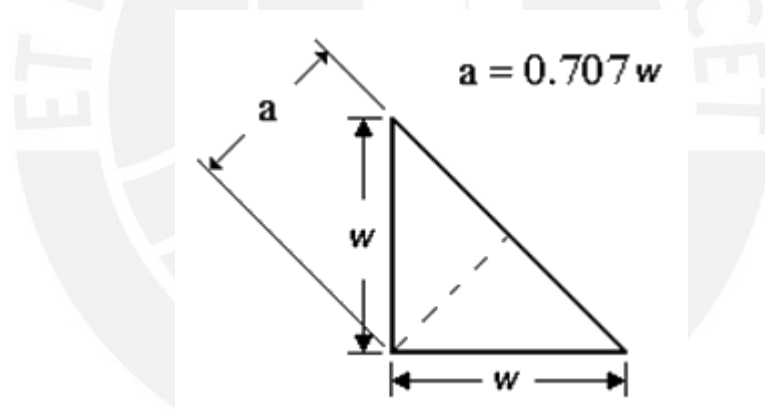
[8] Representación de la sección del cordón de soldadura.
